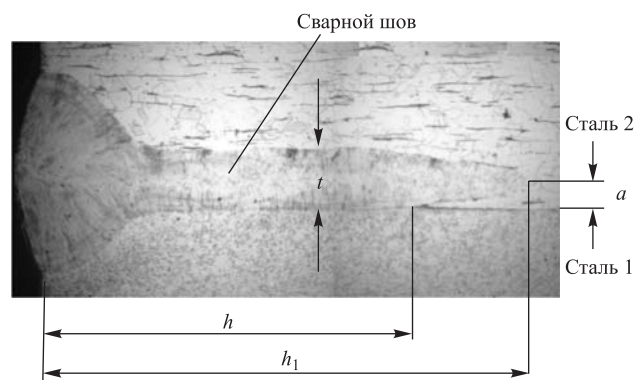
Характерный вид сварного шва, выполненного электронно-лучевой сваркой
